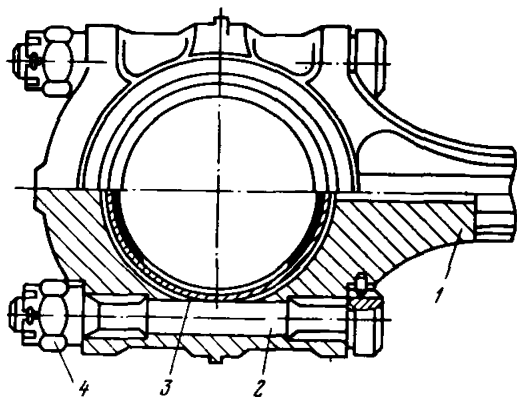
Большая головка шатуна компрессора 4ВМ10-100/8:
